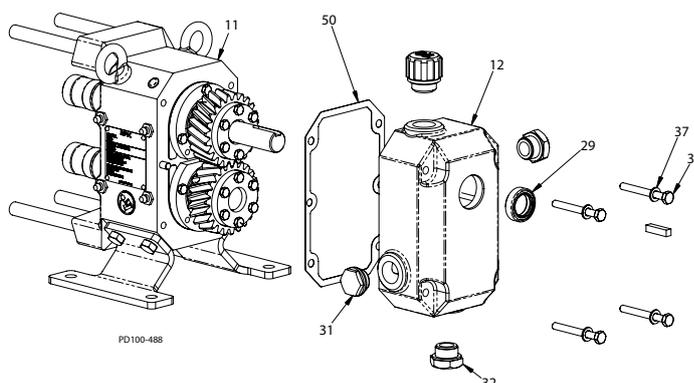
Retirez le couvercle de la boîte d'engrenages
